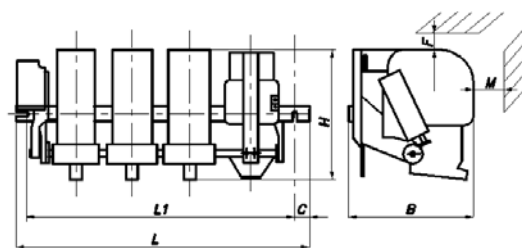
Общий вид и габаритные размеры КТ-6000.
